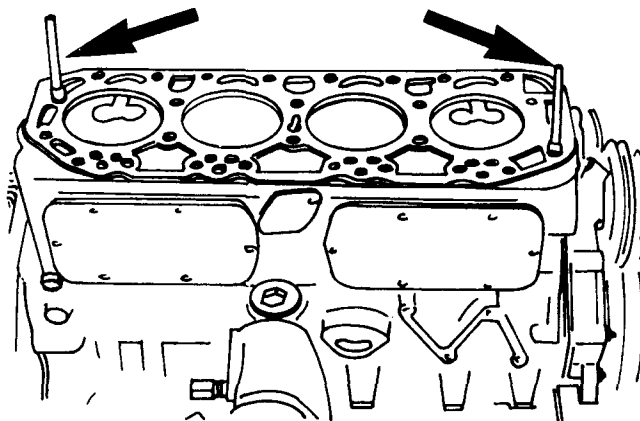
Две направляющие шпильки на блоке цилиндров для установки прокладки и головки блока.
